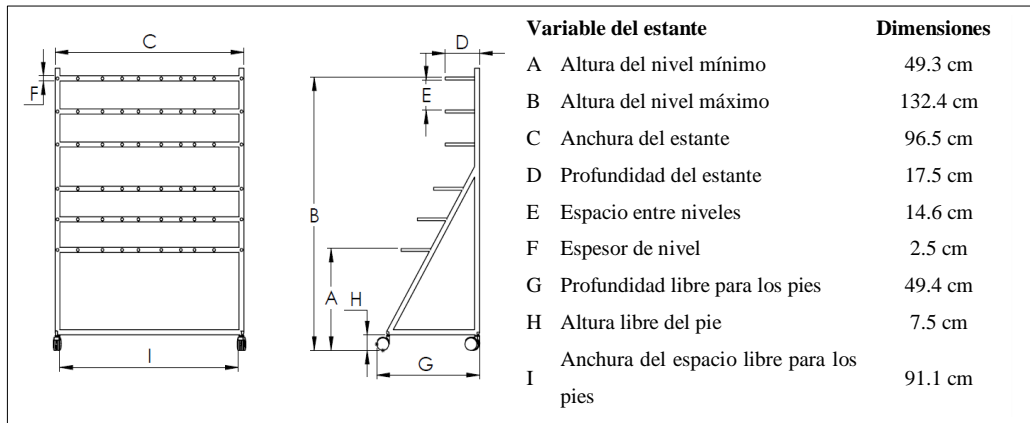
Dimensiones actuales del estante de corte para posición de pie
